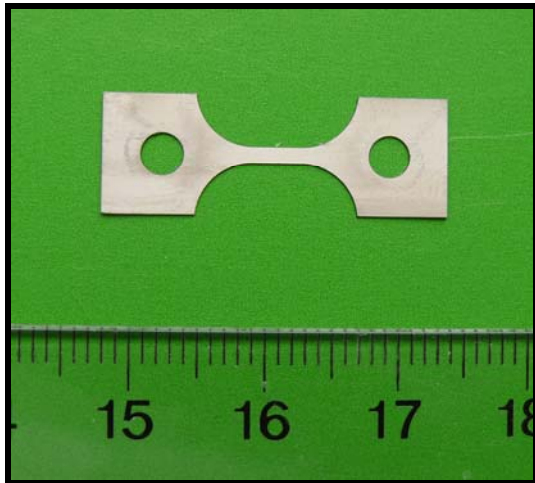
Photographie der verwendeten Zugprobe (aus einem Blech hergestellt)
